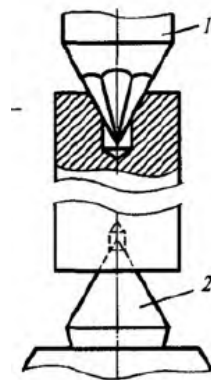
Схема чистового оброблення центрувальних отворів:
